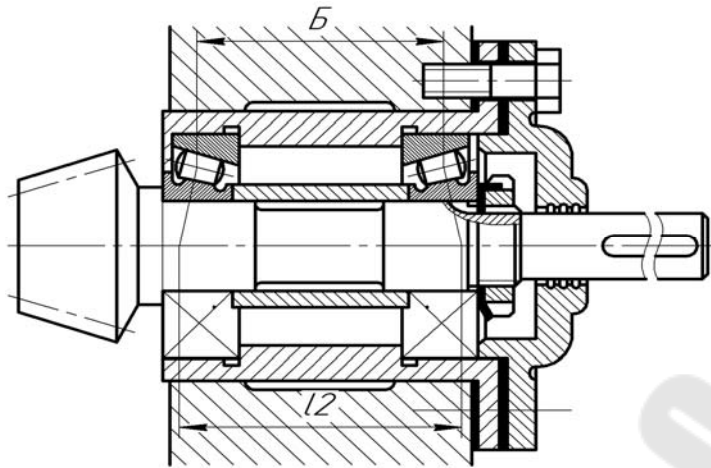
Подшипниковый узел на конических роликоподшипниках (вариант, допускающий температурные удлинения вала)
